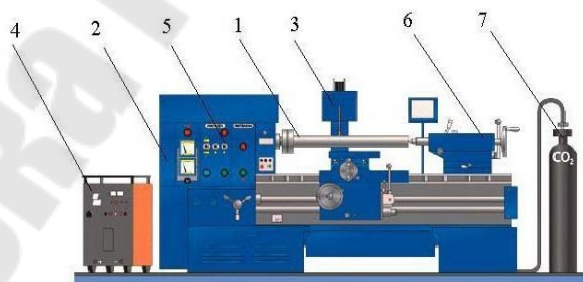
Схема типовой установки для автоматической наплавки цилиндрических деталей порошковой проволокой: 1 – наплавляемая деталь; 2 – манипулятор-вращатель; 3 – сварочная головка; 4 – источник питания; 5 – пульт управления; 6 – задняя бабка; 7 – баллон с защитным газом
